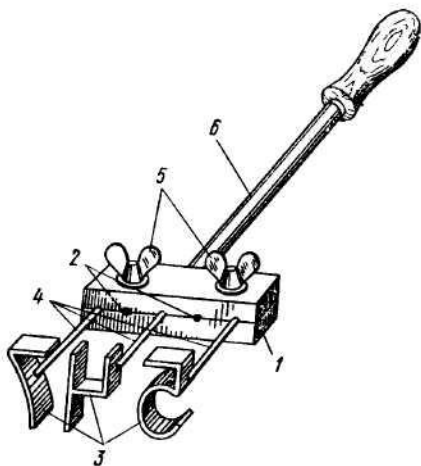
Приспособление для мечения рыб: 1 – державка; 2 – отверстие для закрепления матриц; 3 – матрицы; 4–штоки; 5 – винты; 6 – рукоятка
